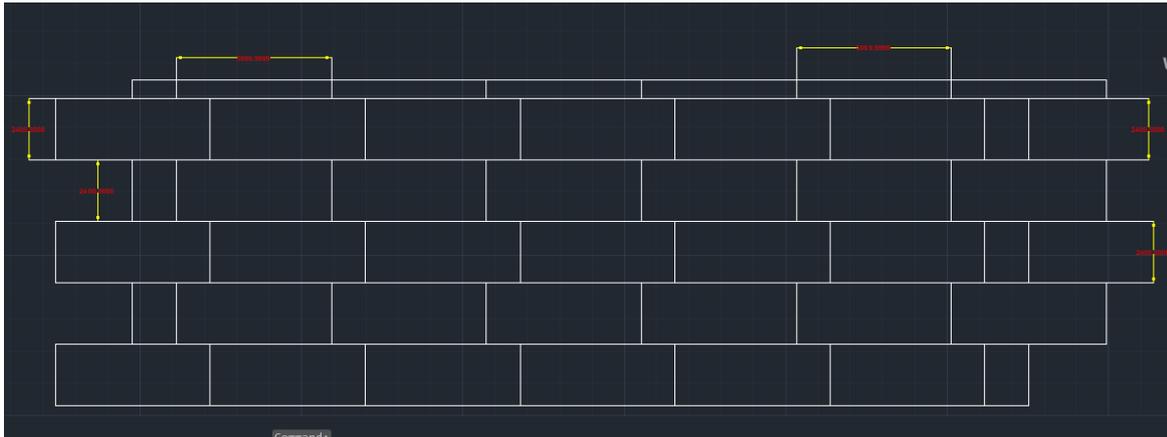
Mapa de soldadura del casco de un tanque (caso de proyecto sin mejora)
